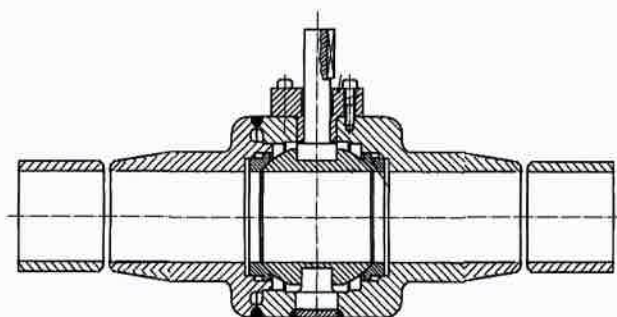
Esquema de instalación para soldadura, todas las válvulas vienen preparadas para soldar
